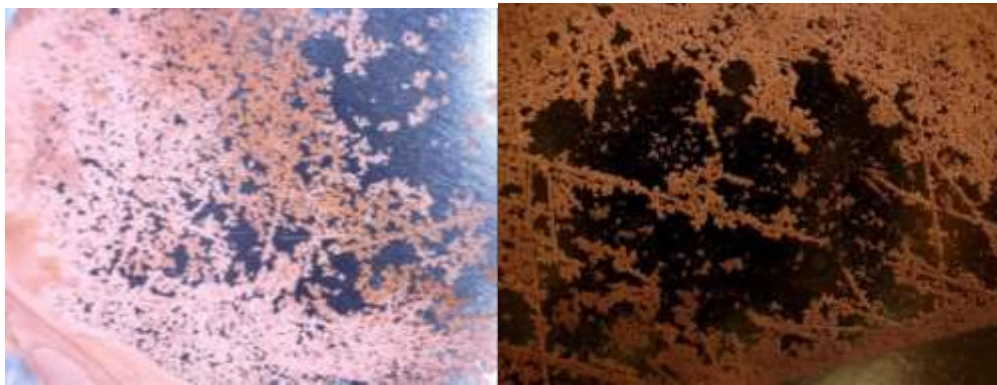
Поверхность заготовки №1 и №2 соответственно
